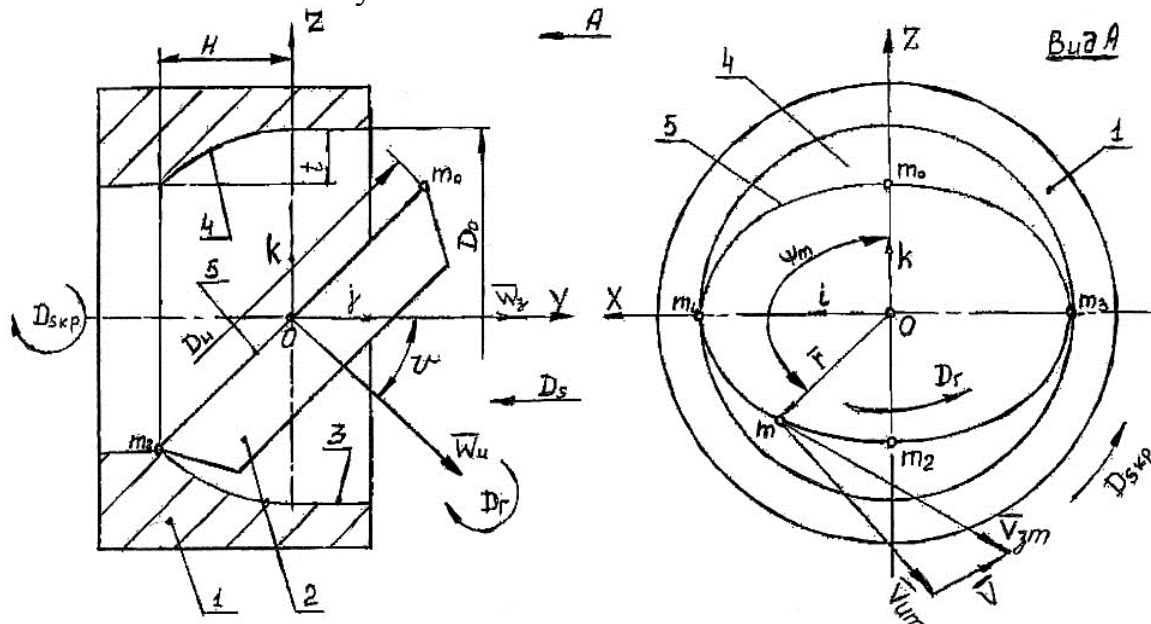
Кинематическая схема свободнообкатного резания с пересекающимися осями.
